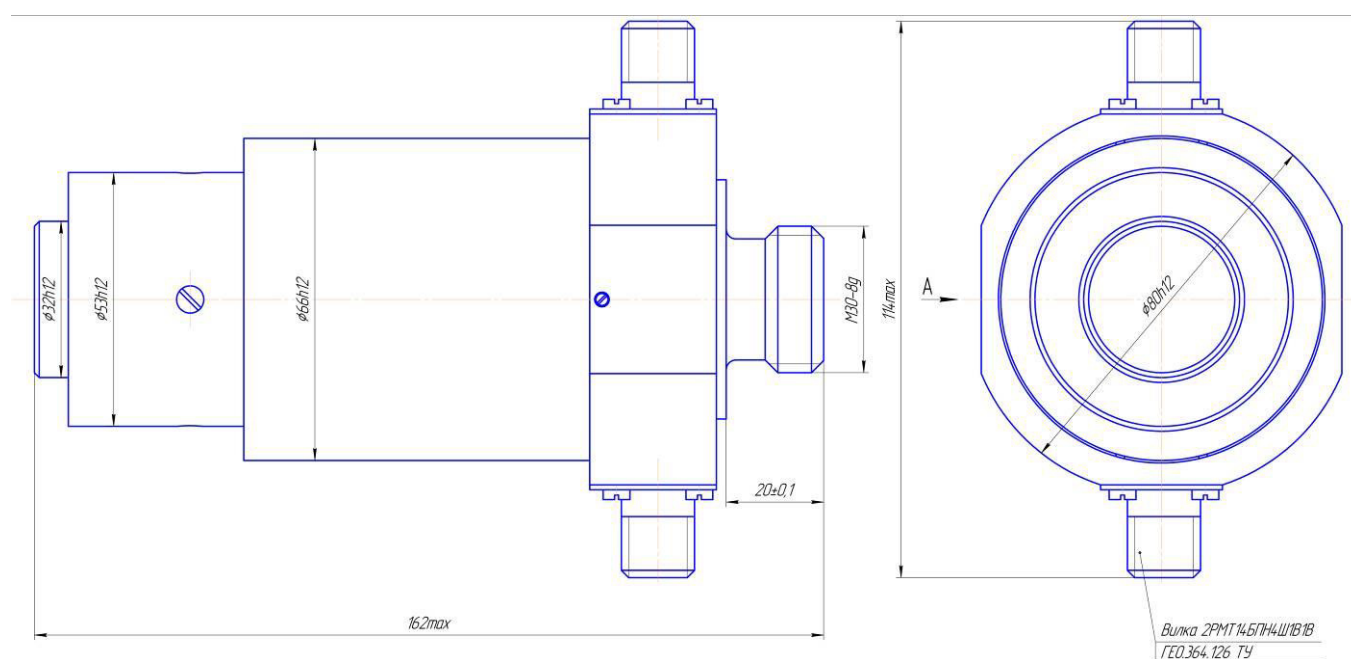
Габаритно-установочные размеры датчика НТ 051
